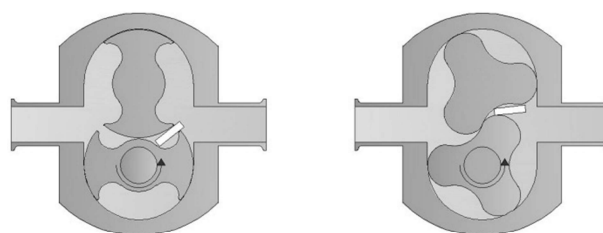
Rotorschrauben lösen (unterer Rotor)
